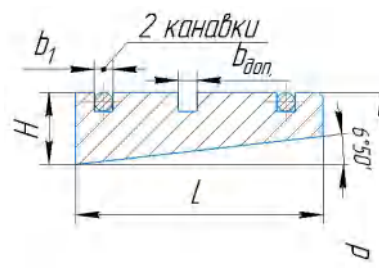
Эскиз кулачка оправки. Посередине есть дополнительная канавка для размещения цельного кольца при обточке по месту.
